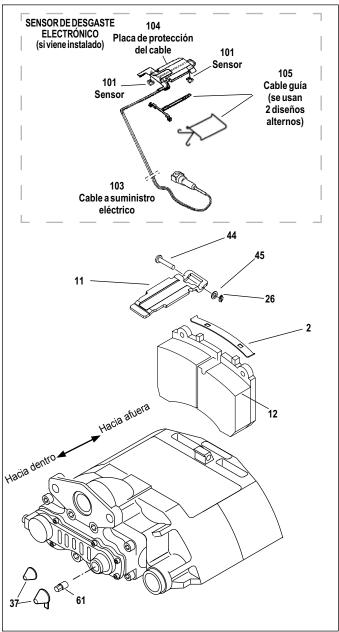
REEMPLAZO DE LAS ZAPATAS
